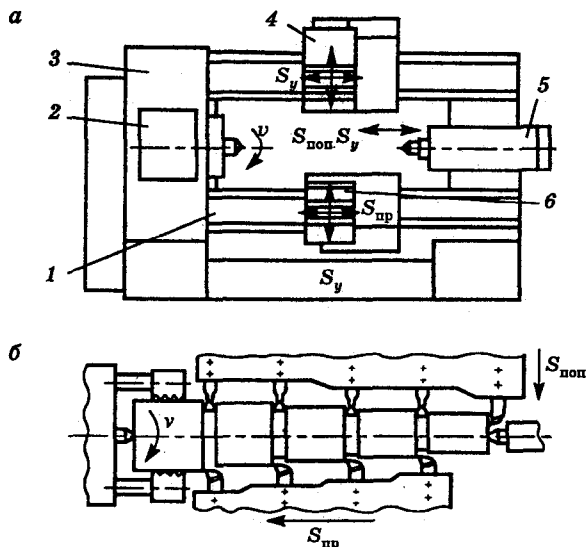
Токарный многорезцовый полуавтомат (а) и обработка на нем заготовки (б)
